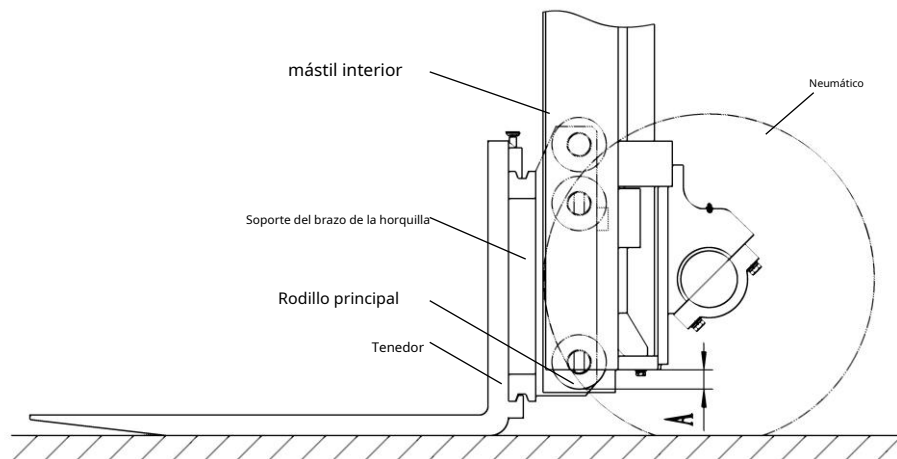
Ajuste de la altura del soporte del brazo de la horquilla
